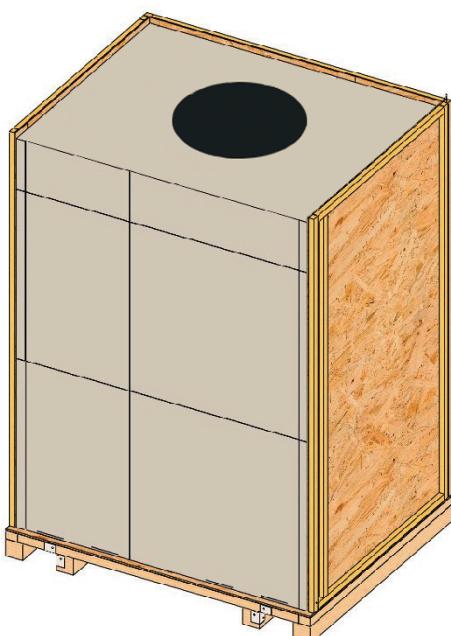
Вид упакованного изделия со снятой верхней и боковой стенками
